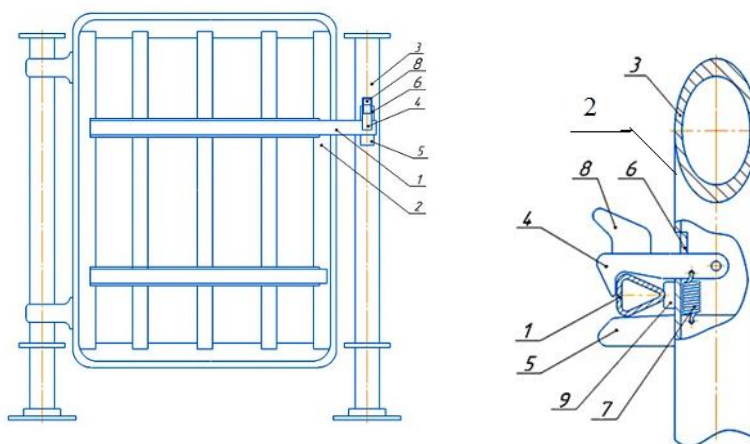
Защелка и для животноводческих станков: 1 – ригель; 2 – дверь; 3 – основа; 4,5 – зацеп; 6 – паз; 7 – пружина; 8 – рукоятка; 9 – упругий элемент
